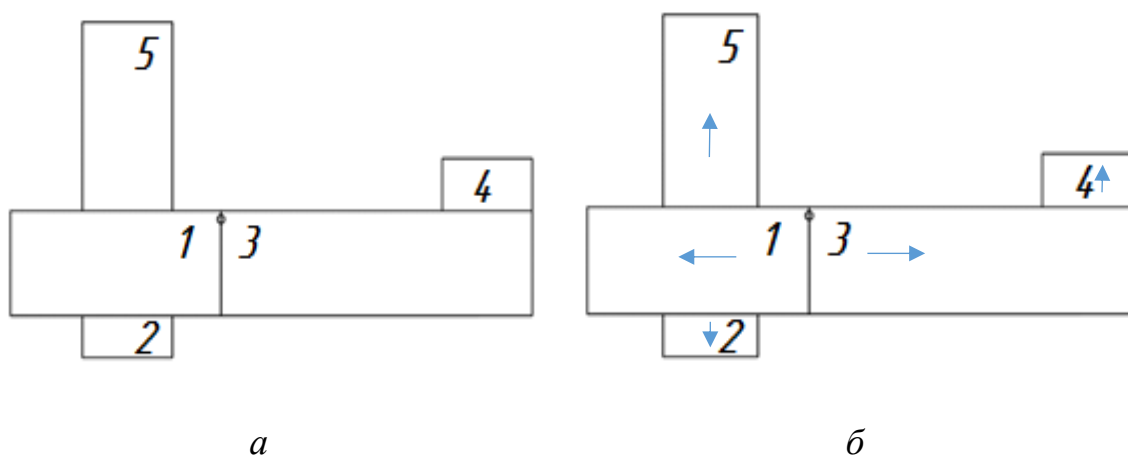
Упрощенный вид корпусной детали (а); схема предполагаемого направления течения расплава из точки инъекции А (б)
